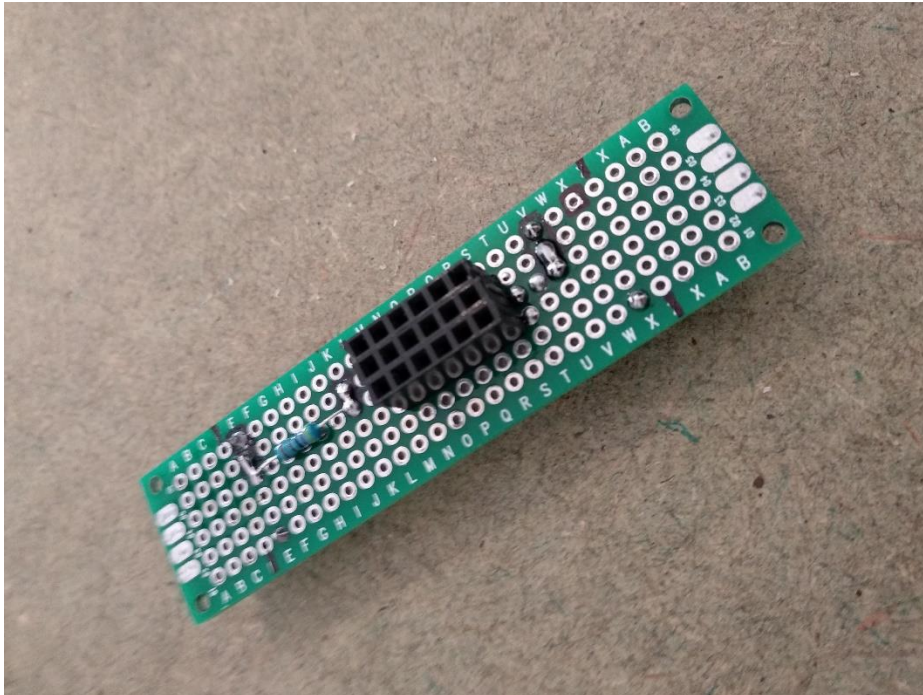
Parte superior de la placa stripboard sin cableado
